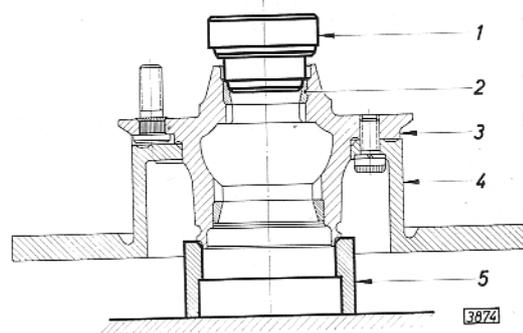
Äußeren Laufring des äußeren Radlagers einpressen
